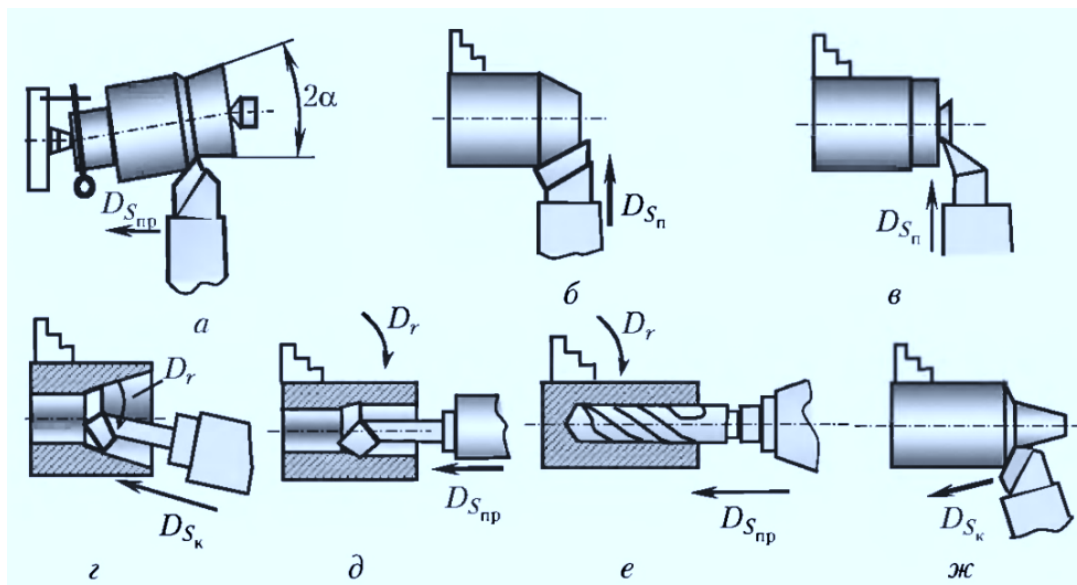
Деякі схеми обробки поверхонь заготовок на токарно-гвинторізному верстаті: а) - зовнішніх конічних поверхонь; б) - коротких конічних поверхонь
